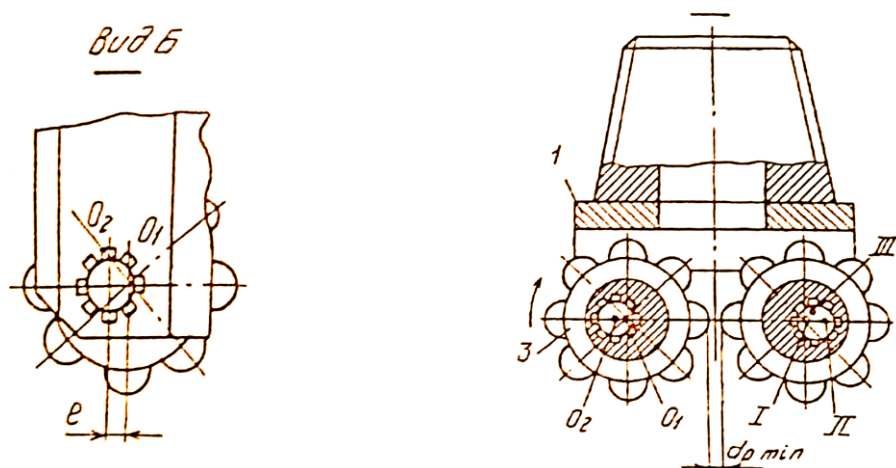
Долото с зубчато-дисковыми шарошками режуще-вращательного типа
